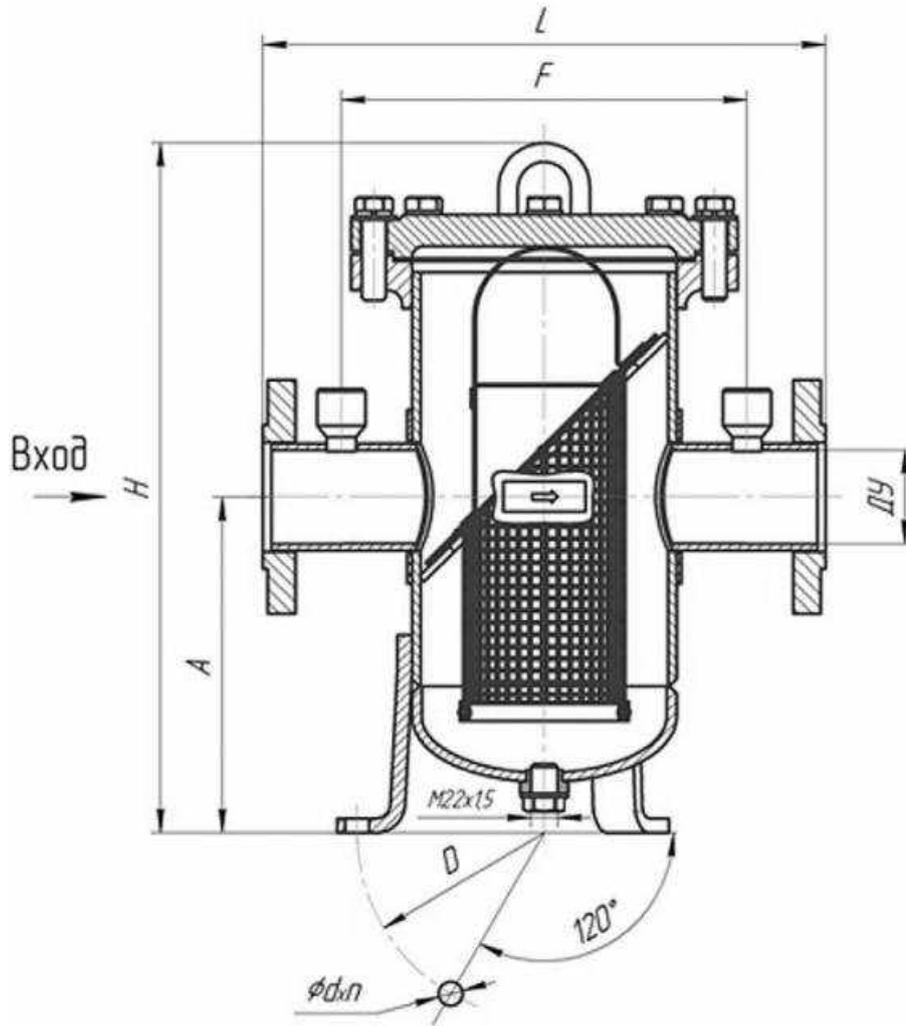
Габаритные и присоединительные размеры фильтров ЭМИС-ВЕКТА 1210 и с креплением крышки по периметру
